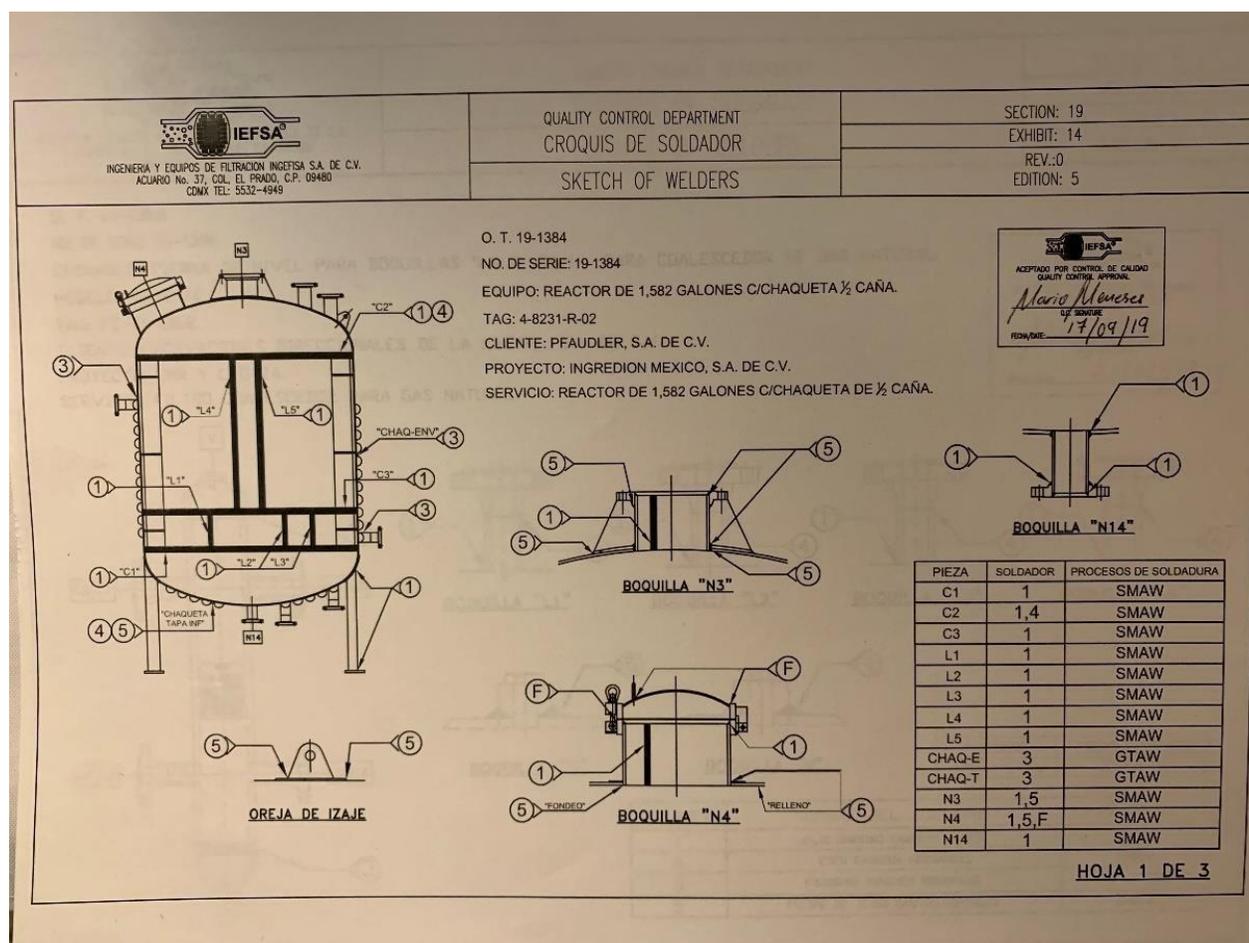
Plano de las líneas de soldadura para reactor.
